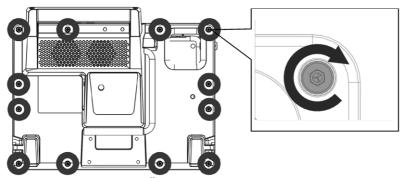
Festziehen der Gehäuseschrauben 🛈 um den Rehadapter™ zu schließen
